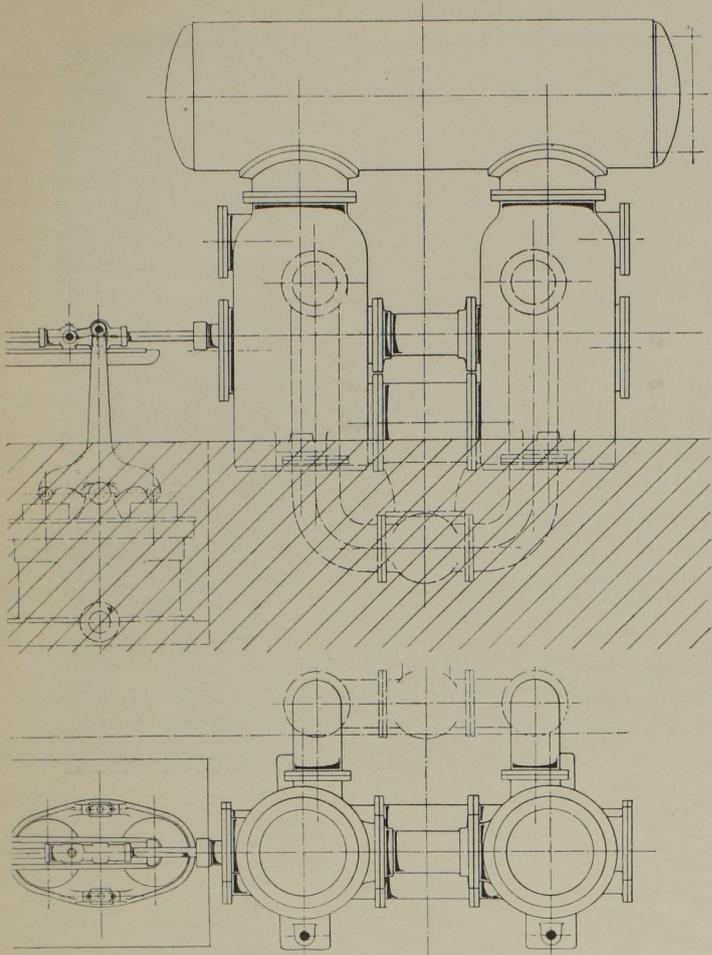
Grundriss und Aufriss der Pumpe. Masst. 1:50.
